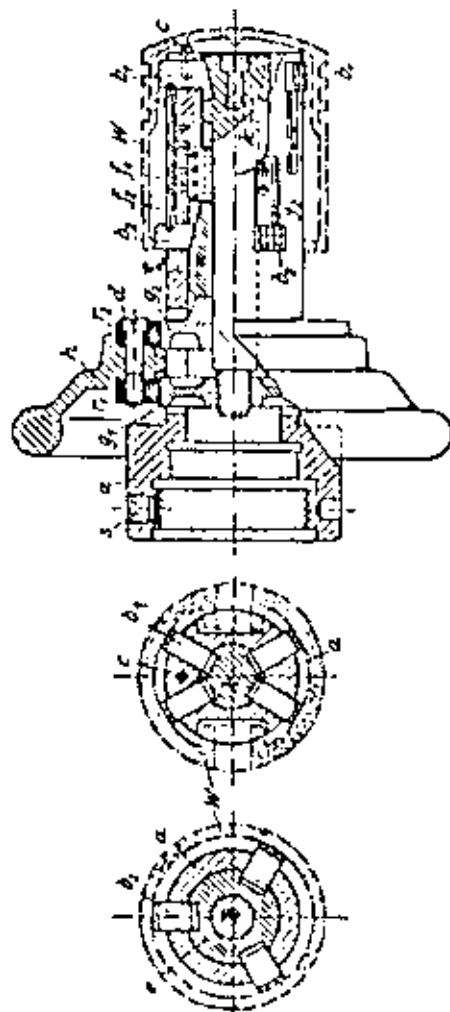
Dispositivo de sujeción para el torneado de émbolos de motor. a, cuerpo; b1 y b2, garras; c, tope; d, tornillo; e, pieza de presión; f1 y f2, lengüetas; g1 y g2, piezas roscadas; h, volante de mano; k, pieza de sujeción; r1, tuerca de rosca a la derecha; r2, tuerca de rosca a la izquierda; s, tornillo de seguridad con pieza de presión; W, pieza.
